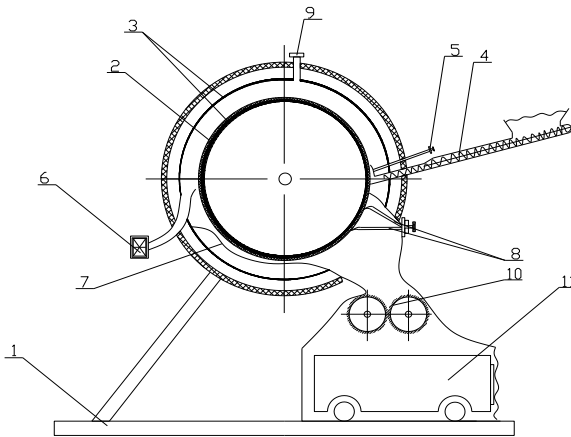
Вальцьова ІЧ-сушарка безрефлекторного типу безперервної дії для сушіння багатокомпонентних плодово-ягідних напівфабрикатів: 1 – опора; 2 – рифлений барабан; 3 – ГПРЕНВТ; 4 – нагнітаючий шнек із прямокутною цавкою; 5 – прижимний пристрій із підпружиненою пластиною; 6 – нагнітаючий вентилятор; 7 – захисний екран; 8 – зрізаючі ножі; 9 – патрубок відведення пари; 10 – накопичувальна ємність
